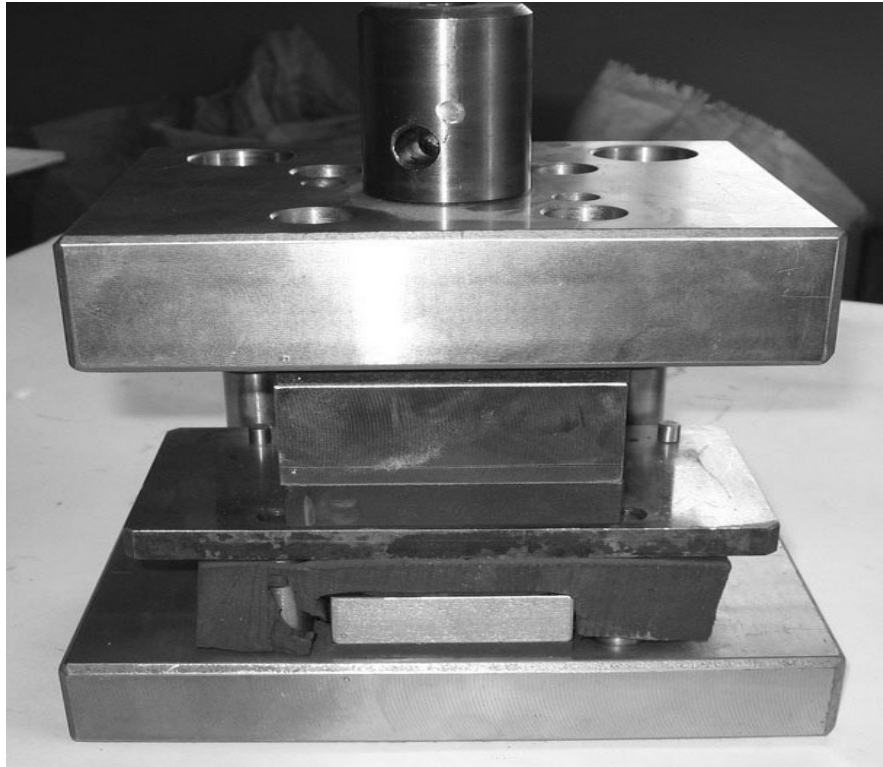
Штамп в металі виготовлений з штамп - напівфабрикату
